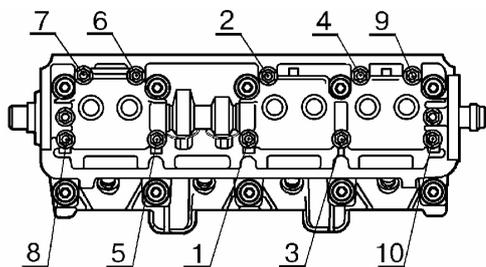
Порядок затяжки гаек крепления корпусов подшипников распределительного вала двигателя ВАЗ-21114.
